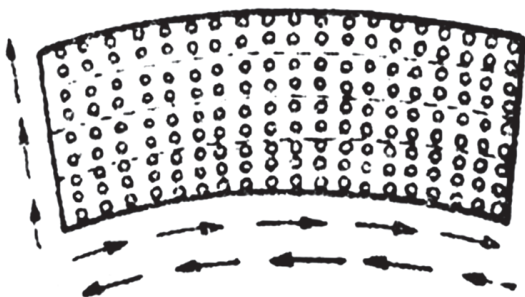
Схема правки изогнутости заготовки на ребро
